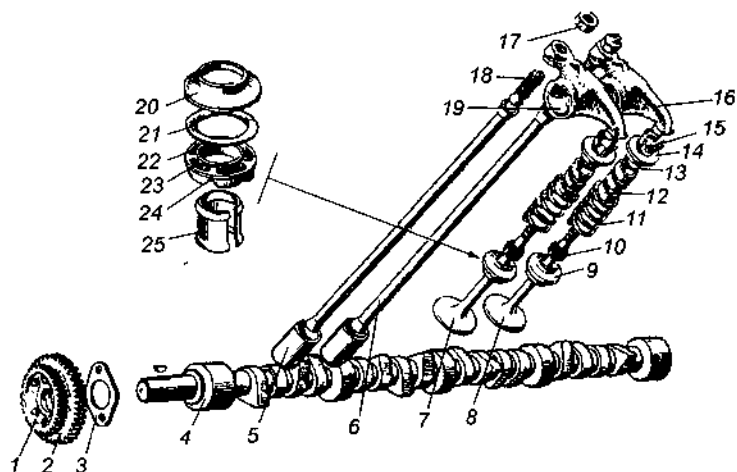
Газораспределительный механизм двигателя: 1 — зубчатое колесо привода топливного насоса; 2 — зубчатое колесо распределительного вала; 3 — фланец; 4 — распределительный вал; 5 — толкатель; 6 — штанга; 7 — выпускной клапан; 8 — впускной клапан; 9 — механизм вращения клапана; 10 — резиновая манжета; 11 — пружина клапана; 12 — гаситель вибрации пружины; 13 — уплотнительное кольцо; 14 — тарелка; 15 — сухарь; 16 — коромысло; 17 — контргайка; 18 — регулировочный винт; 19 — втулка коромысла; 20 — обойма; 21 — дисковая пружина; 22 — шарик; 23 — пружина; 24 — корпус механизма вращения; 25 — фиксирующая втулка
